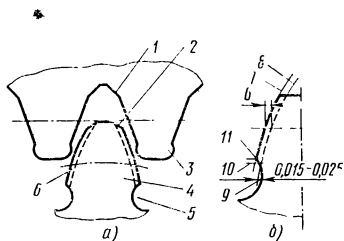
Модифицированная форма зубьев инструмента и колеса:
